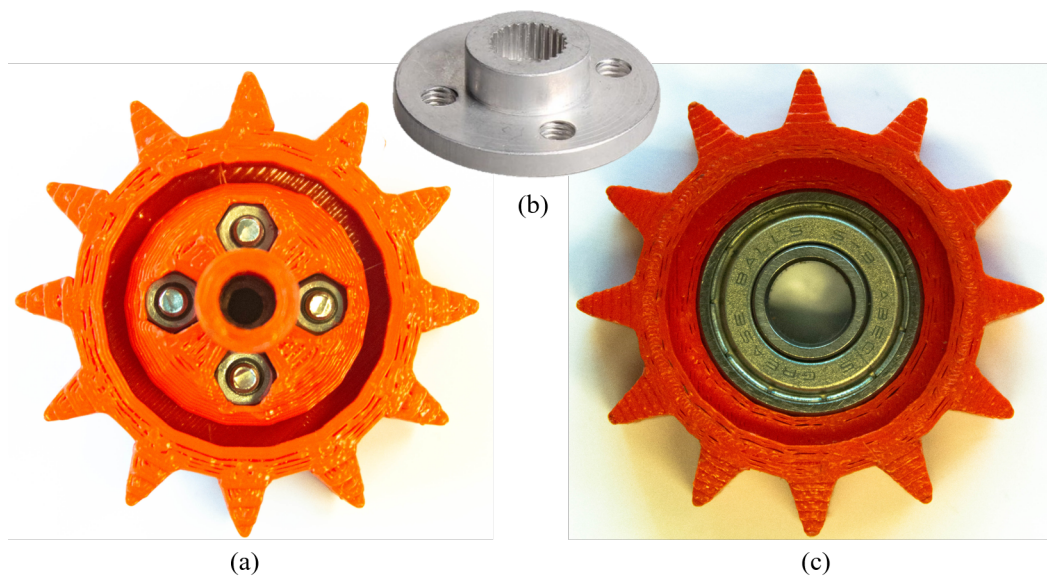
Engranajes fabricados para la la movilización de las cadenas.(a) Engrane motor, (b) Acople metálico circular para fijar el engrane al motor y (c) Engrane con rodamiento.
